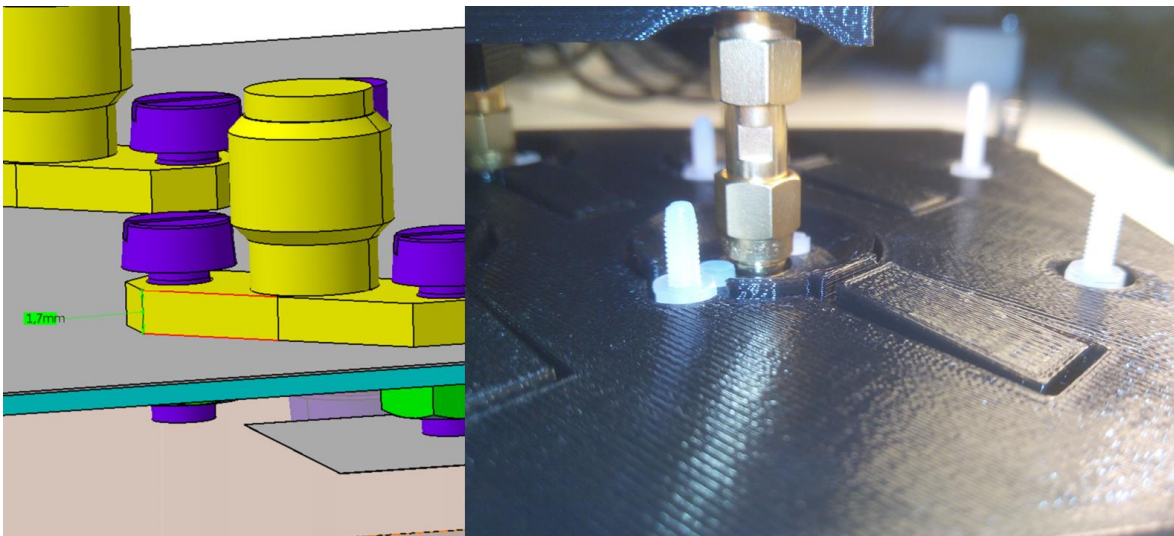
Array fabricado. Detalle del fleje adaptador de la brida de los conectores
